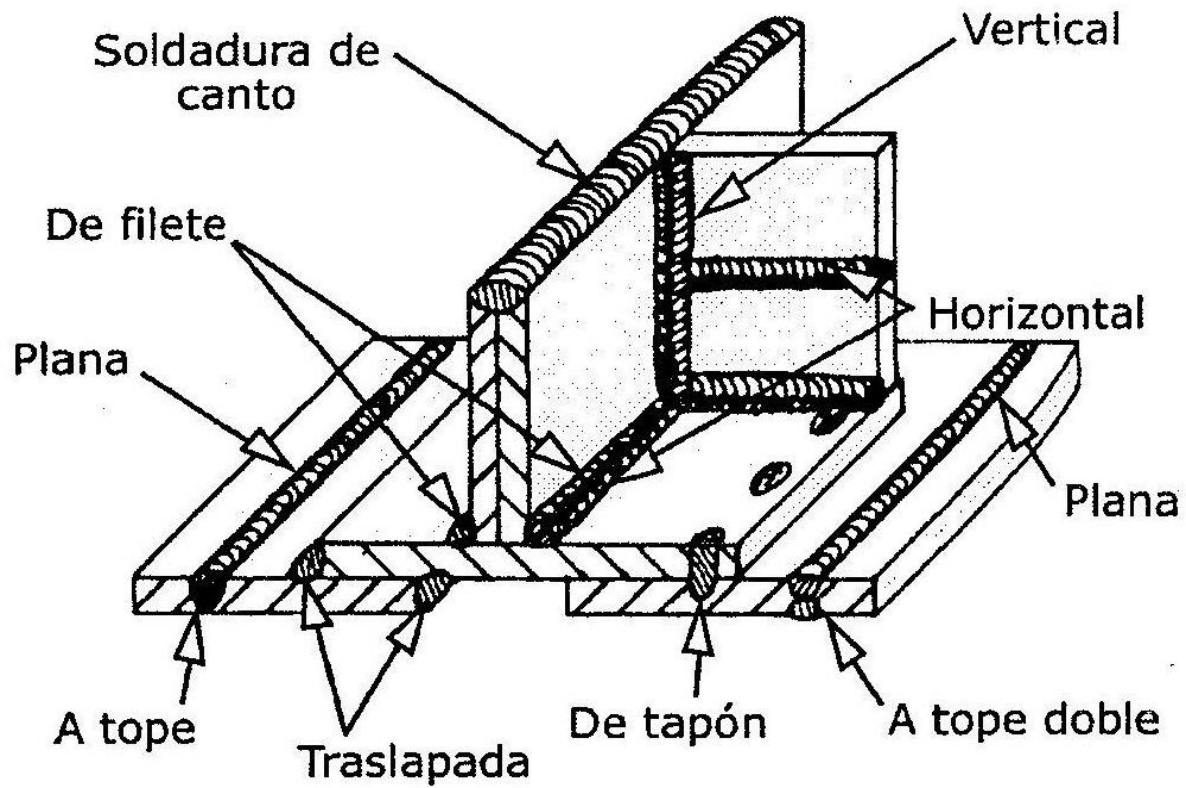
Denominación de los tipos de soldadura
